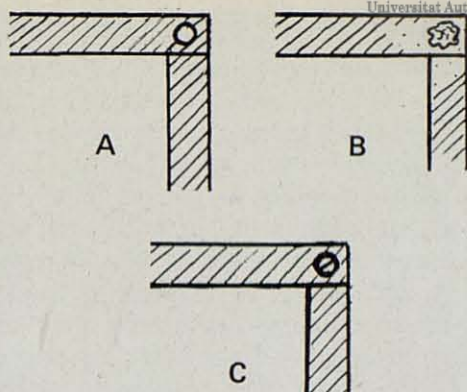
Unión de elementos de plancha galvanizada. A: por remache; B: por punto de soldadura. C: por tornillo. La unión B destruye la protección por causa del calor del punto de soldadura.
